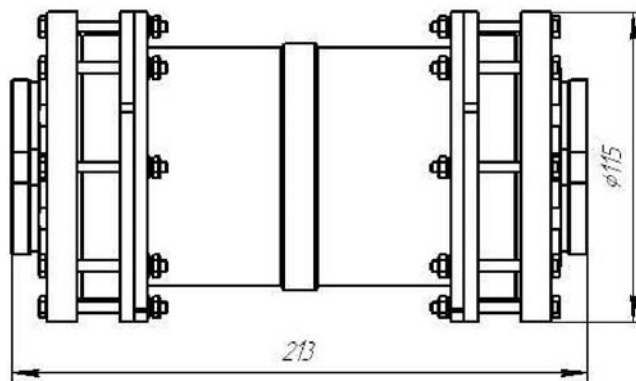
Компоновочне креслення міцного корпусу керування
